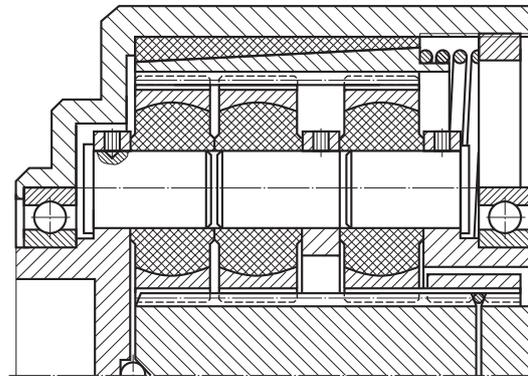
Планетарная передача типа 2К-Н с трехрядным расположением сателлитов и консольными их осями
